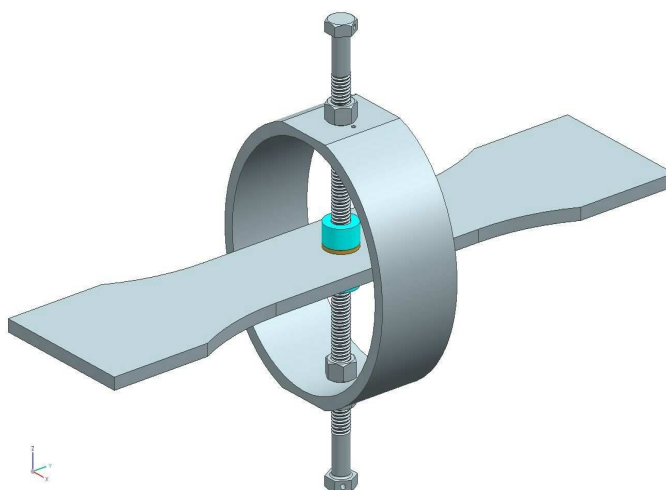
Трехмерная модель образца с приспособлением для проведения усталостных испытаний
